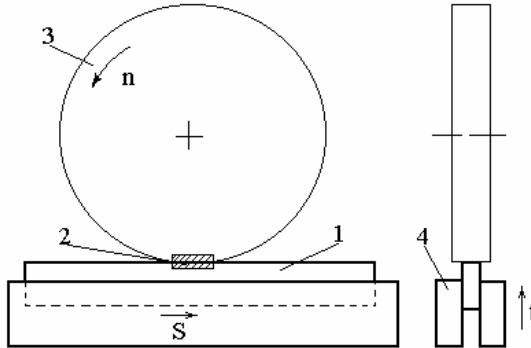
Схема зміцнення ФРЗО: 1 – зміцнююча пластина; 2 – зона контакту; 3 – зміцнювальний диск; 4 – опорні елементи пристрою
